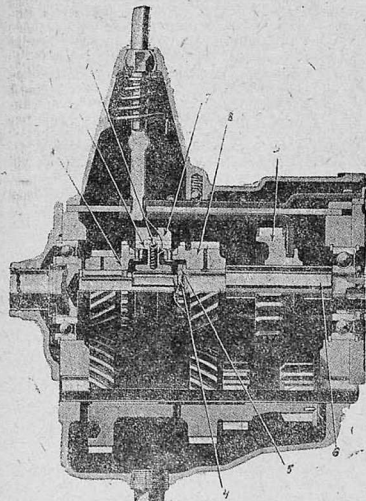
Коробка передач с синхронизатором и бесшумной второй передачей. 1—стопор синхронизатора, 2—подвижная шестерня, 3—прямое зацепление, 4—стопор упорной шайбы, 5—упорная шайба, 6—вторичный вал, 7—подвижная муфта, 8—шестерня второй передачи, 9—подвижная шестерня первой передачи и заднего хода.
